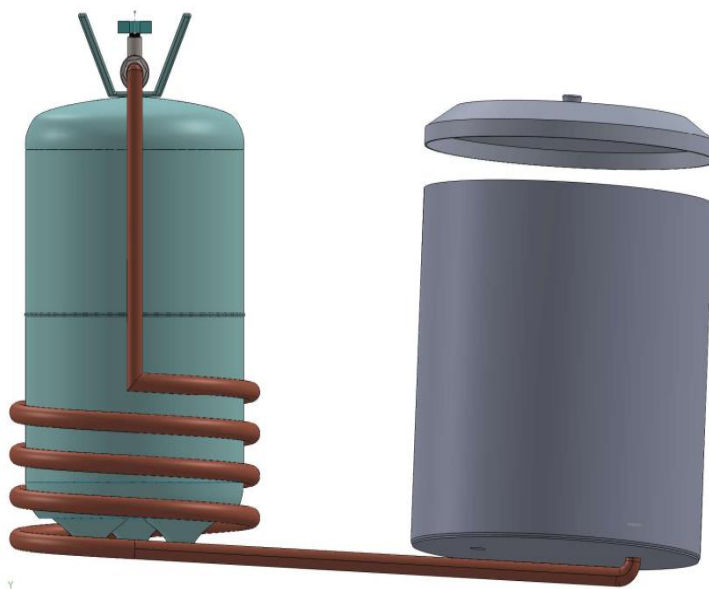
Vue 3D du dessin d'ensemble de l'étuveuse à vapeur
